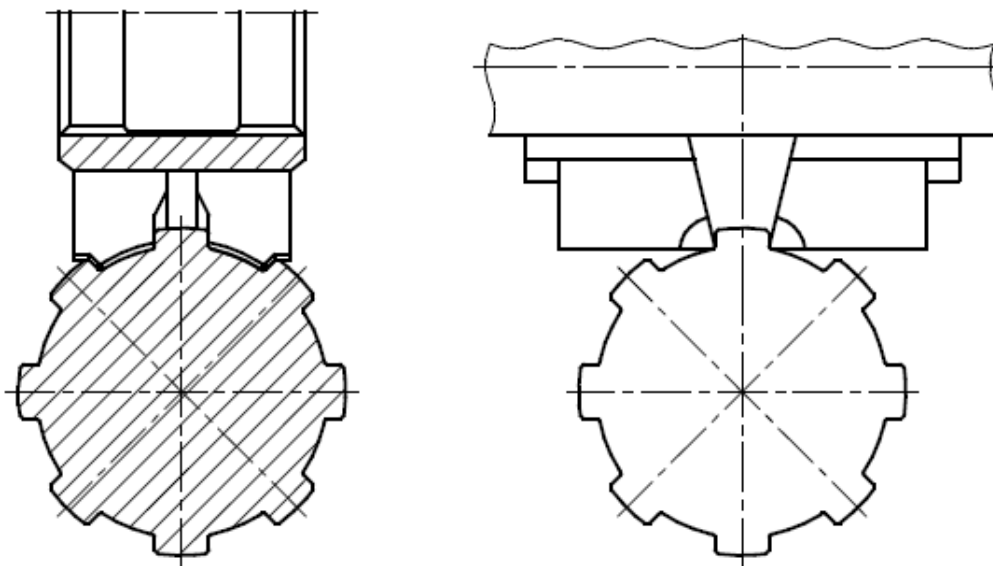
Обробка шліців фасонною та торцевою фрезами
